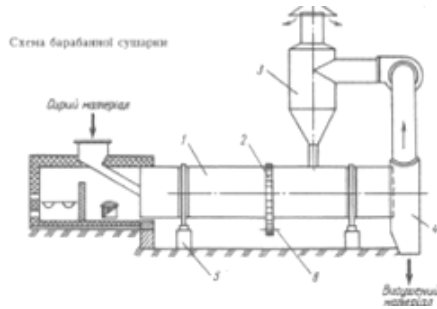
Принципова схема барабанної сушарки:
